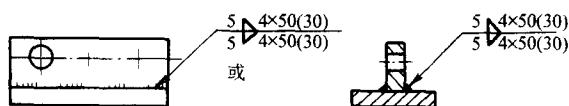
用图示法绘出焊缝的焊缝符号标注
